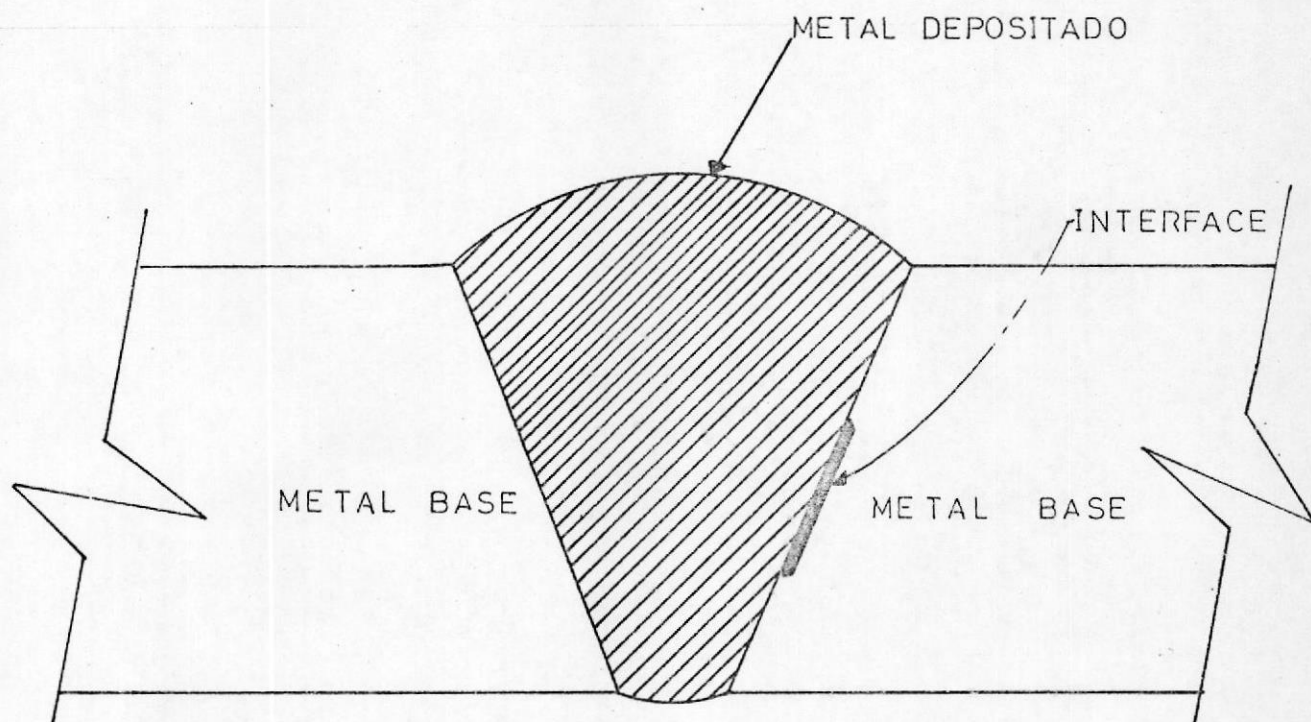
FALTA DE FUSION EN UN PROCESO DE SOLDADURA AL ARCO. (10)
